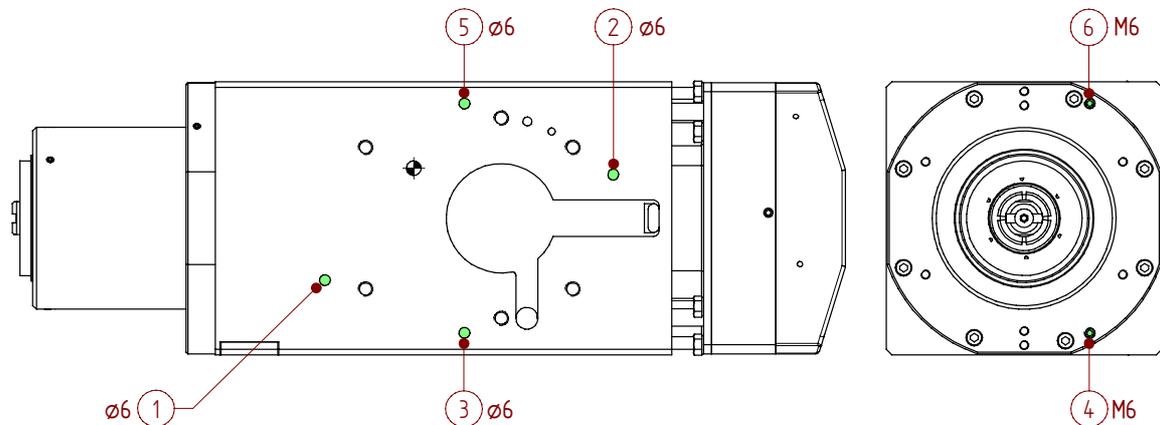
hydraulische anschlüsse für ES789 mit Befestigungsnuten
